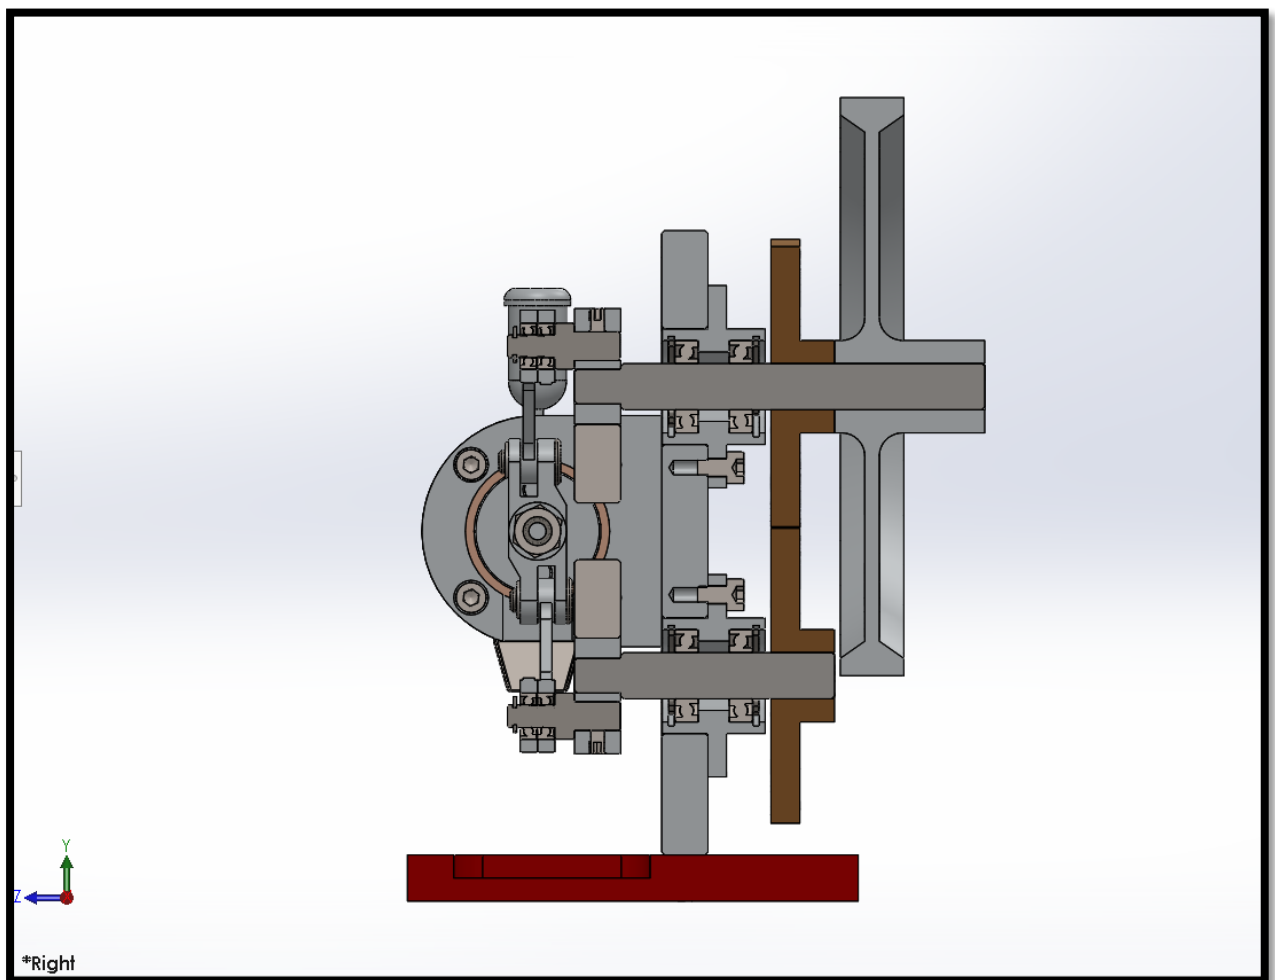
Vista de perfil del conjunto en SolidWorks.
